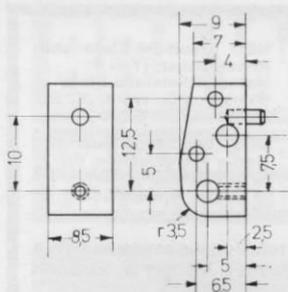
Bauzeichnung für den Zylinderblock und die Kolbenstangen-Schutzrohre im Maßstab 1:1 für H0 (1:87).
